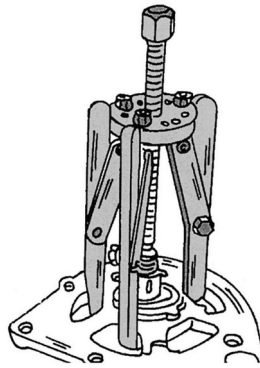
Ви пресування ротора з передньої кришки
